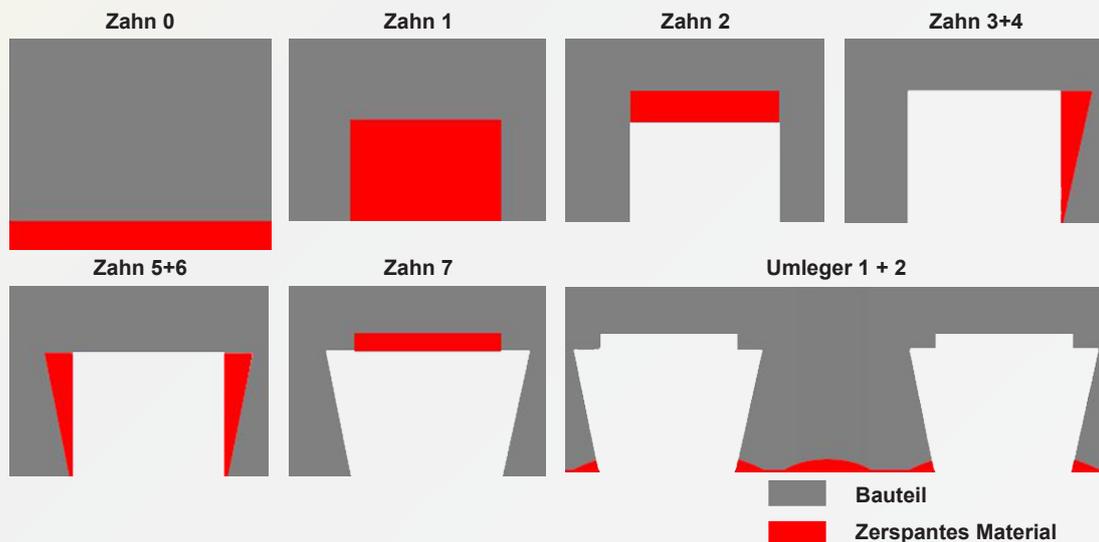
Die Bearbeitung des Bauteils aufgeteilt in die einzelnen Zähne
